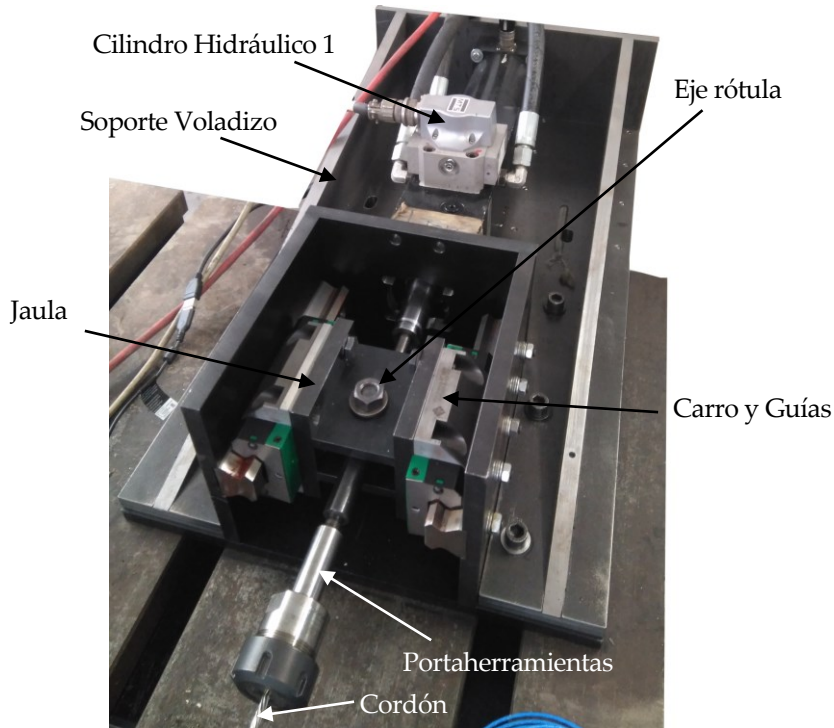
Bloque precarga. Soporte en voladizo con cilindro
